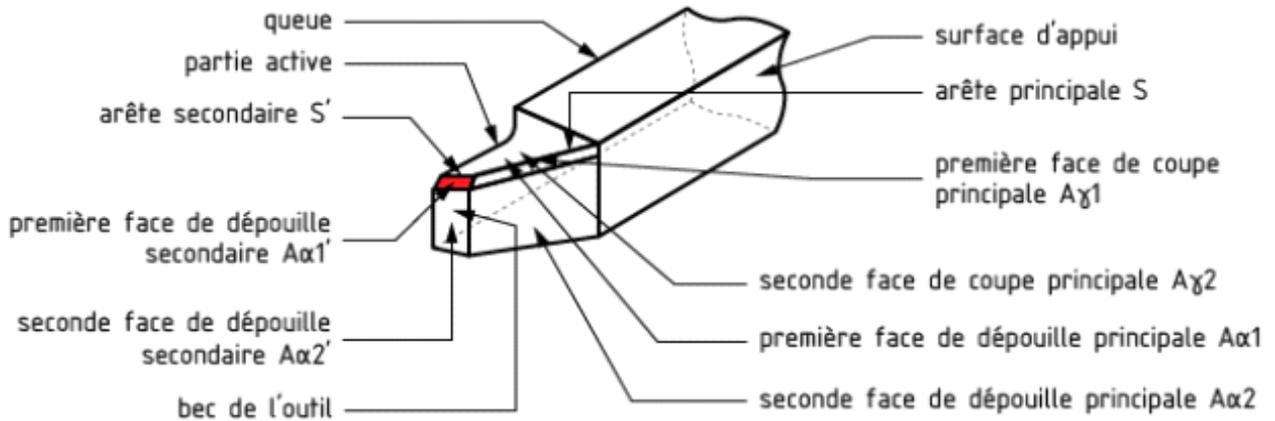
Les principales arêtes et surfaces d'un outil de tournage.
